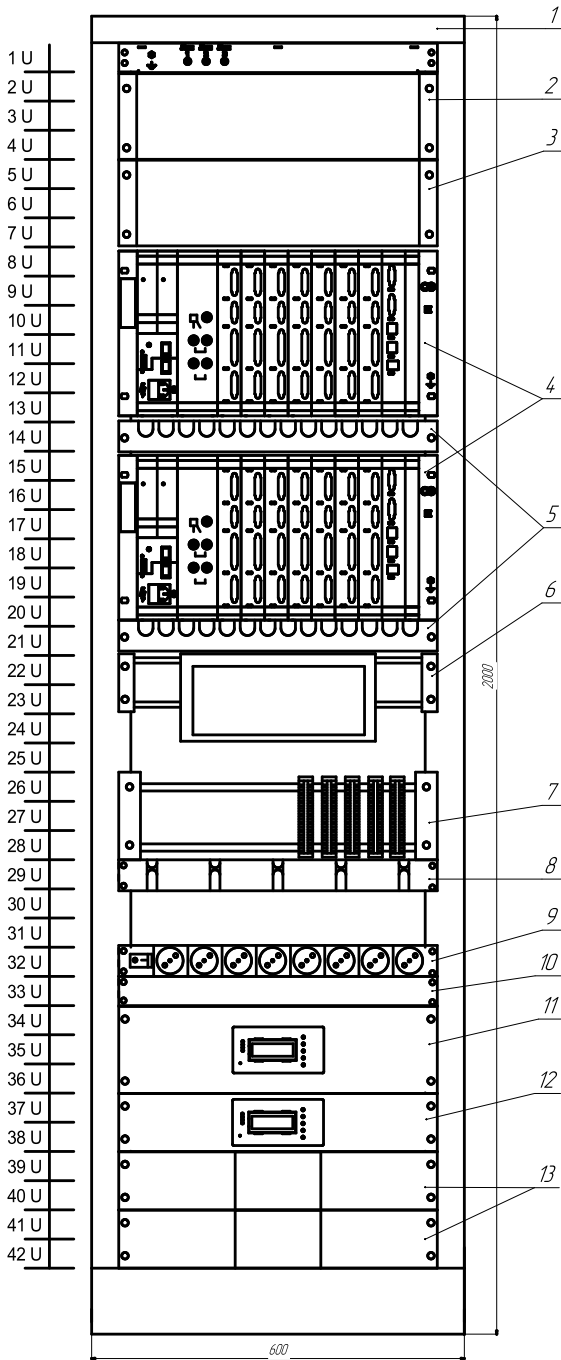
Внешний вид, габаритные размеры передней панели и компоненты напольного шкафа 42U 600×600
